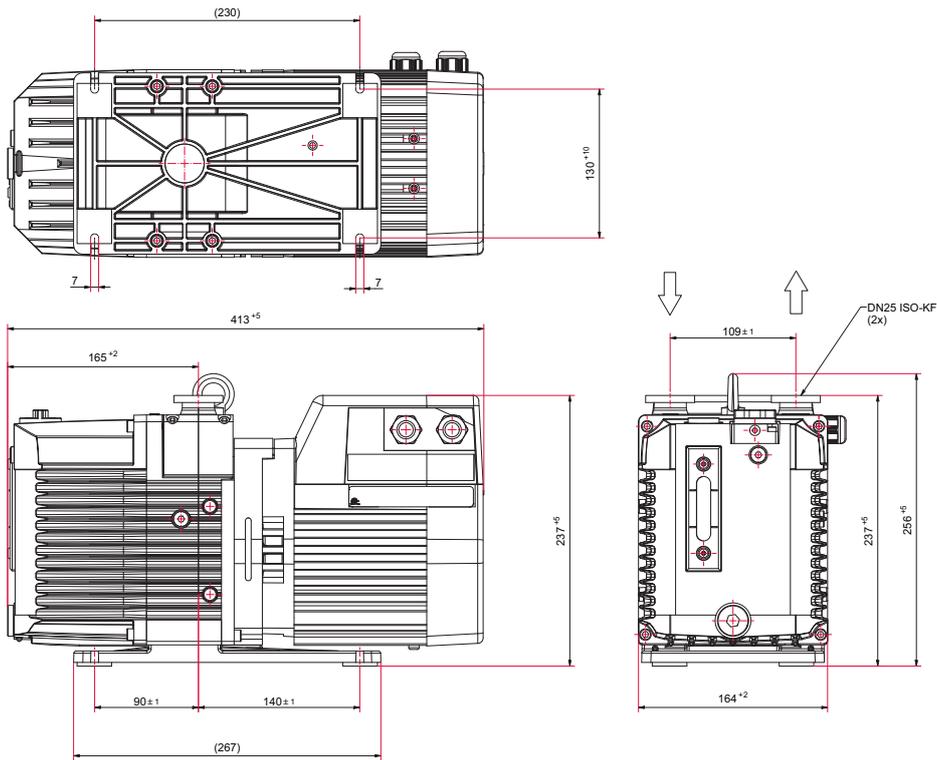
Abmessungen DuoVane 6 mit Dreiphasenmotor
